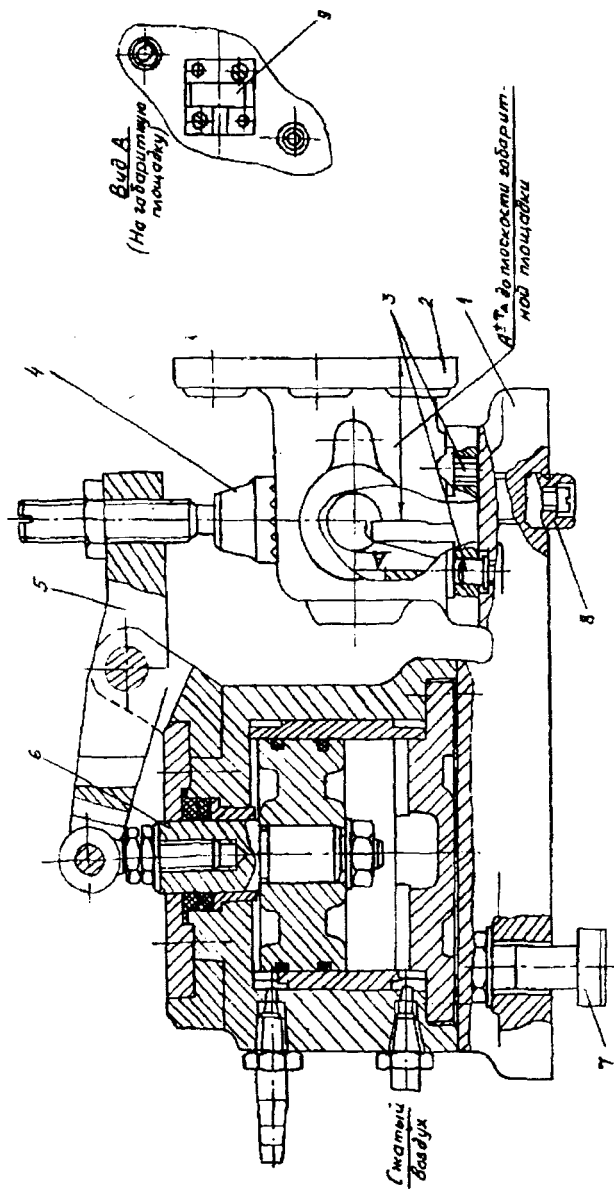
Специальное фрезерное приспособление с пневмоприводом
